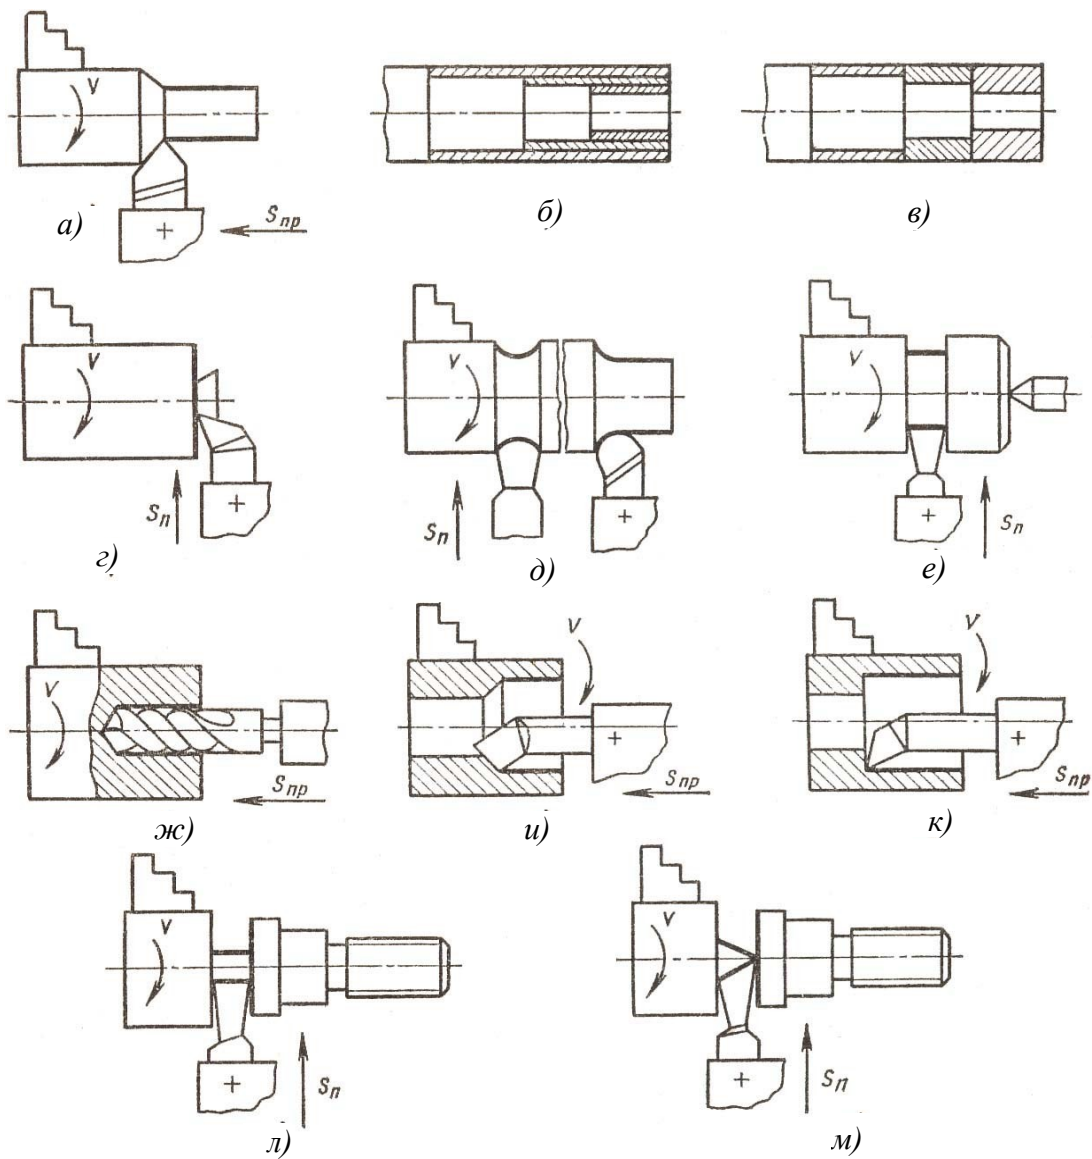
Схеми обробки заготовок на токарно-гвинторізному верстаті
